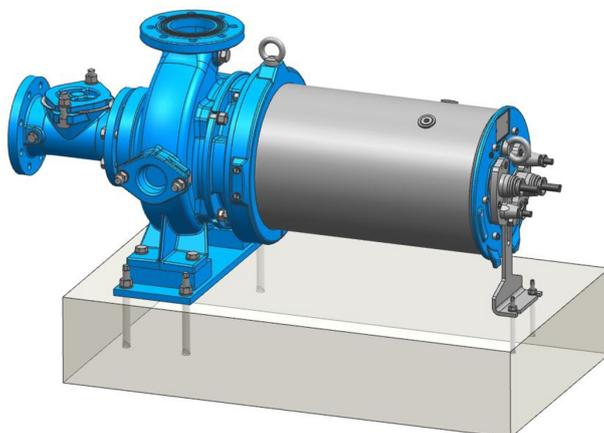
Trockenaufstellung Horizontal; bis Einpass 410; stationär
